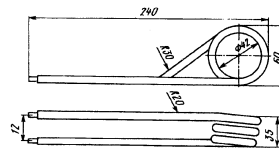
Габаритные и установочные размеры ТЭН-81,7-10-8/1,2x220
